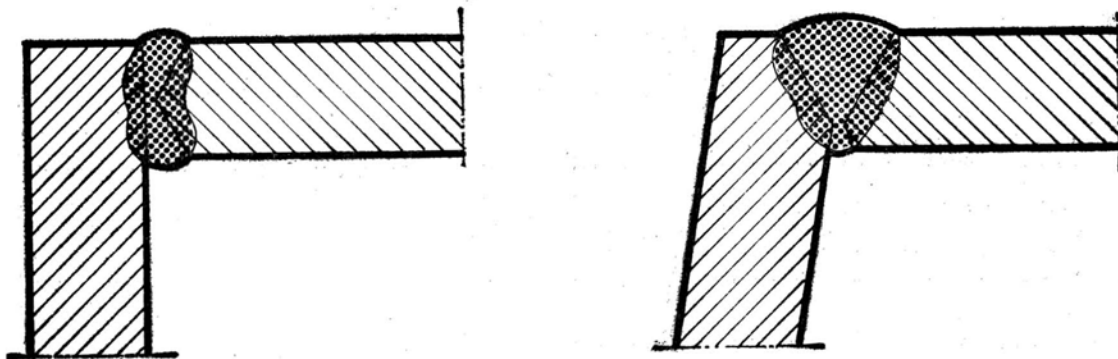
SOLDADURAS A TOPE, EN L
